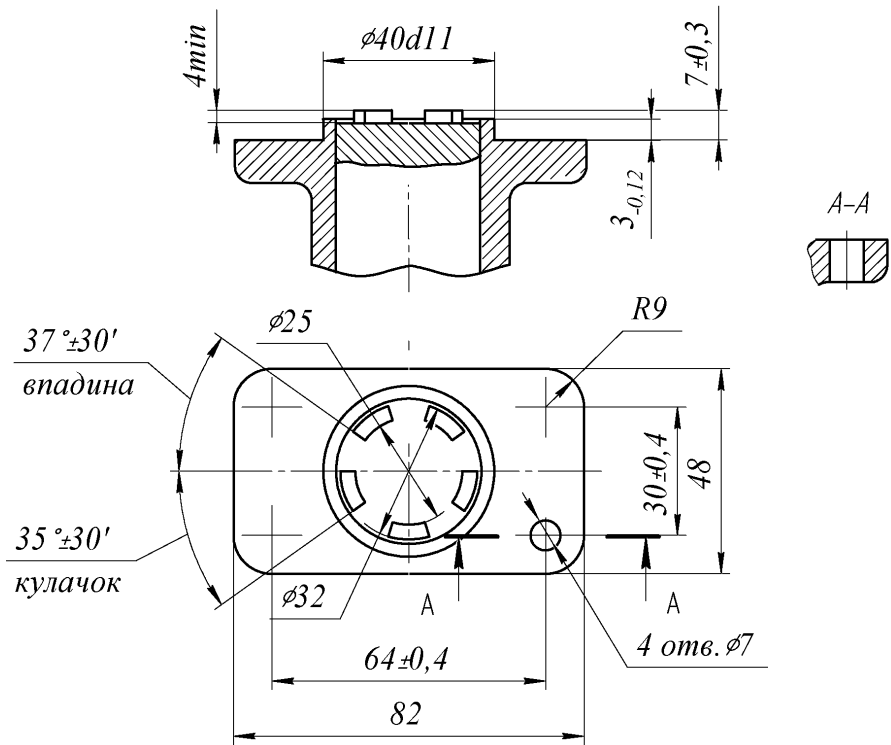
Ответное присоединение трубопроводной арматуры типа АК
